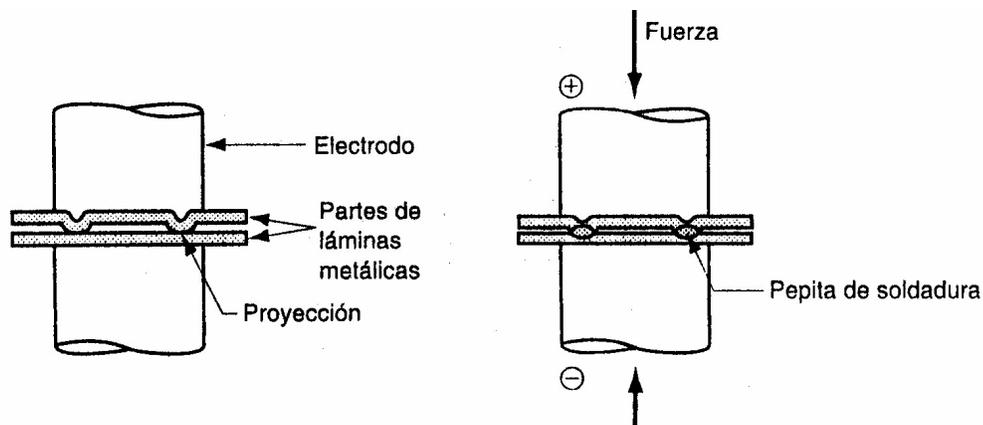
soldadura por proyección (RPW)
